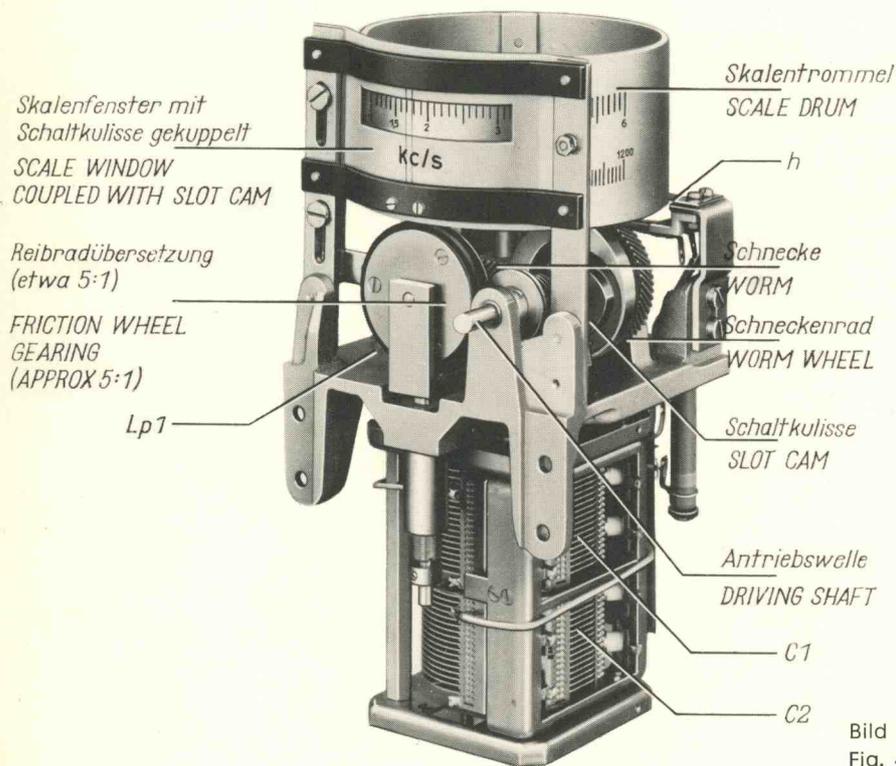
Konstruktiver Aufbau der RC-Baugruppe
